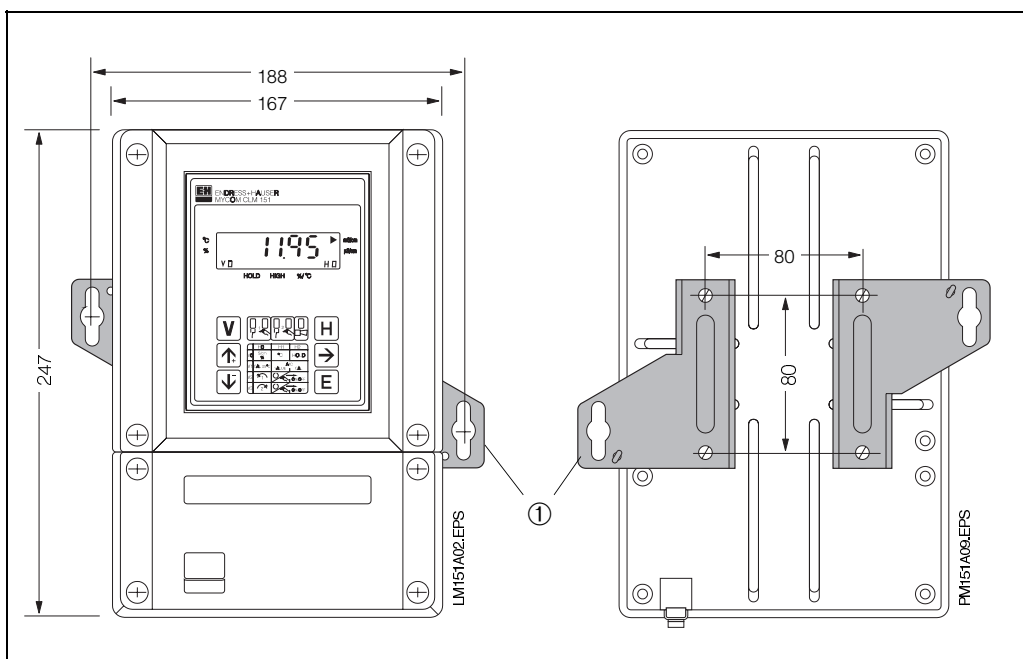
Dimensions du transmetteur (gauche) Mycom CLM 151
